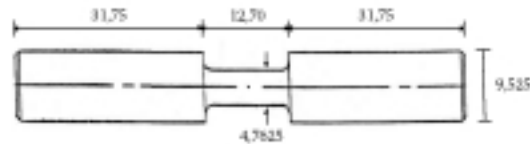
Croqui dos corpos de prova utilizados para ensaios do SAE 1020 - Dimensões mm
